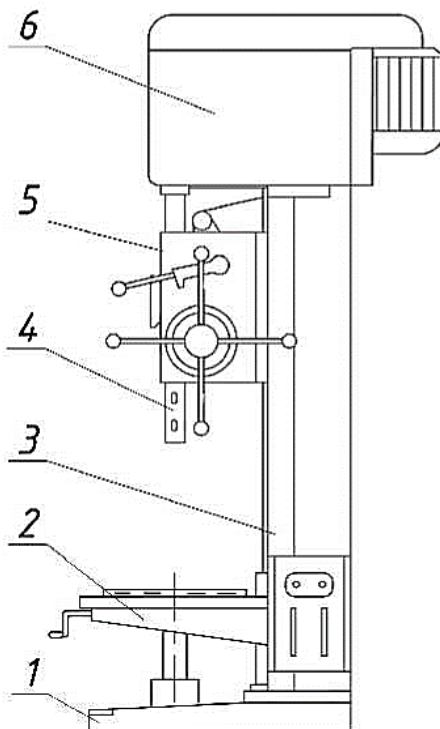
Загальний вигляд вертикально-свердлильного верстата
